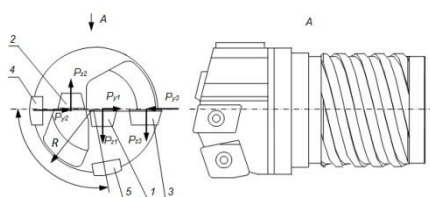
Конструкция головки для глубокого сверления CoroDrill 800.20
